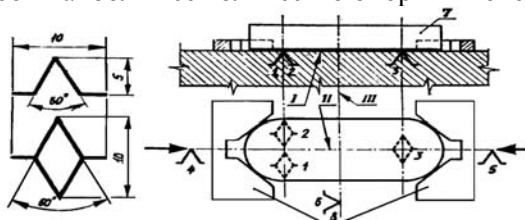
Условное изображение опорных точек (а) и установка заготовки в приспособление по комплекту баз (б):
